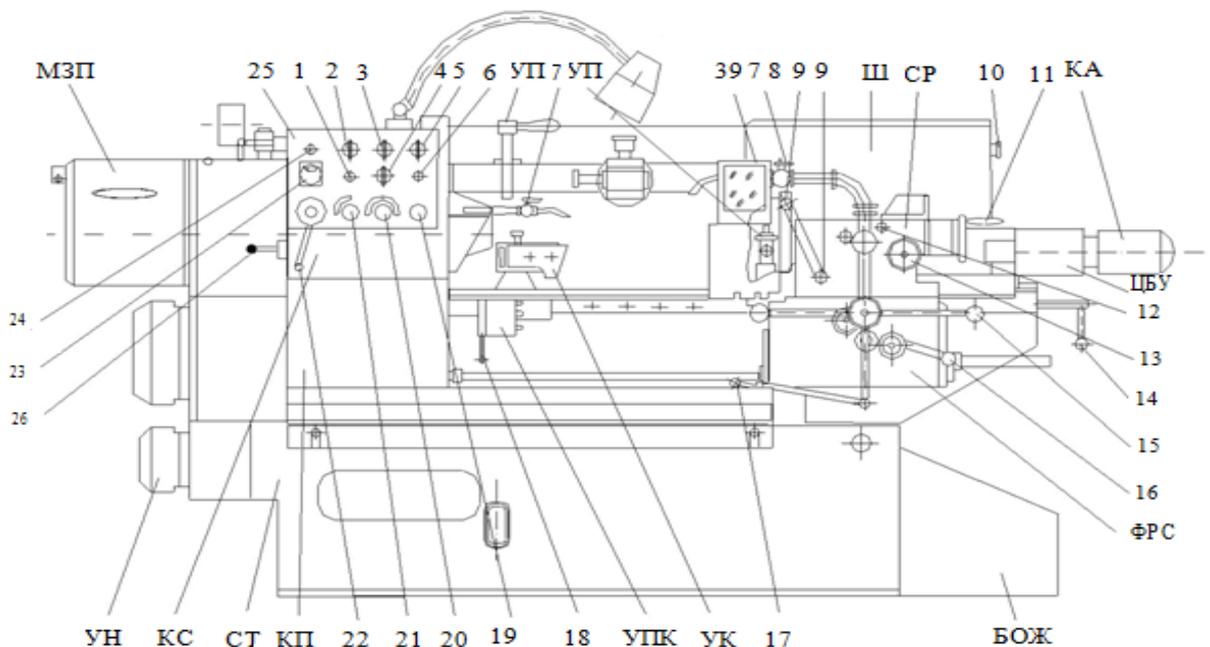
Основные узлы и органы управления токарно-револьверного станка модели 1341
